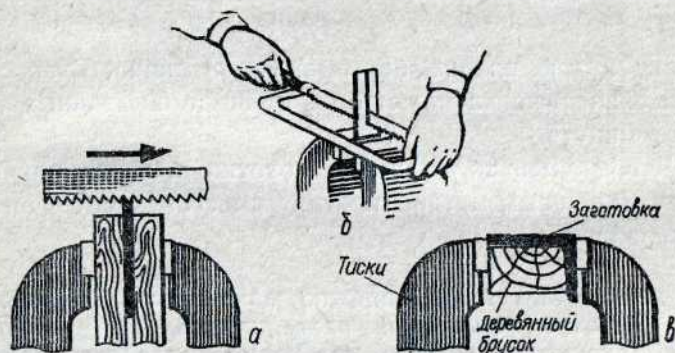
Приемы резания слесарной ножовкой: а — полосового металла; б — длинных заготовок; в — углового металла.
